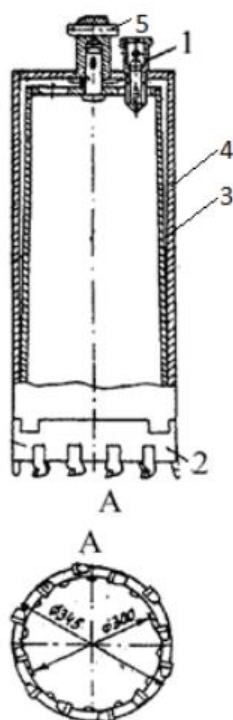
Универсальный кассетный бур БКУ с колонковой кассетой:
